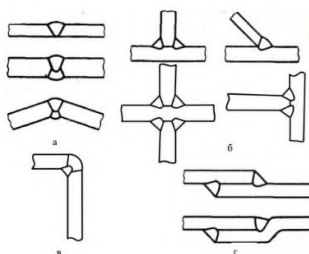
Основные типы сварных соединений: а - стыковые; б - тавровые; в - угловые; г - нахлесточные
